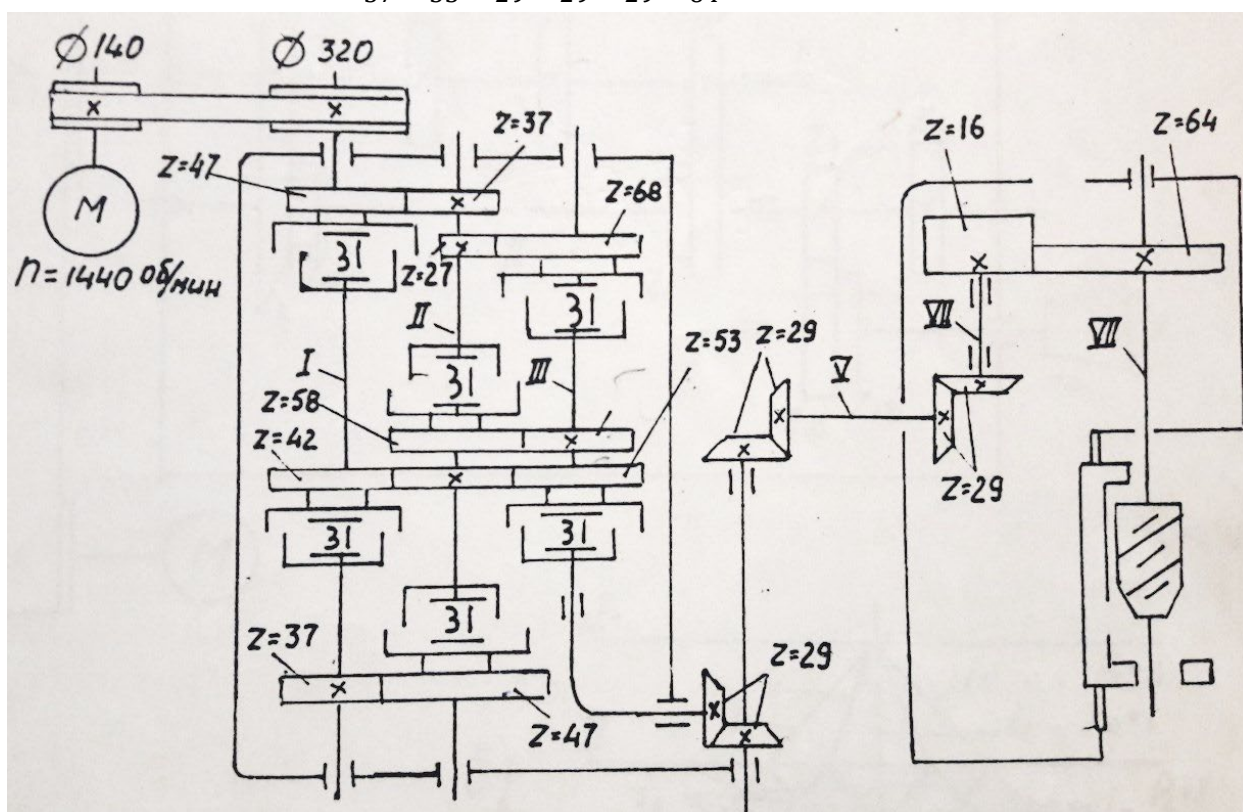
Кинематическая схема коробки скоростей зубофрезерного станка
